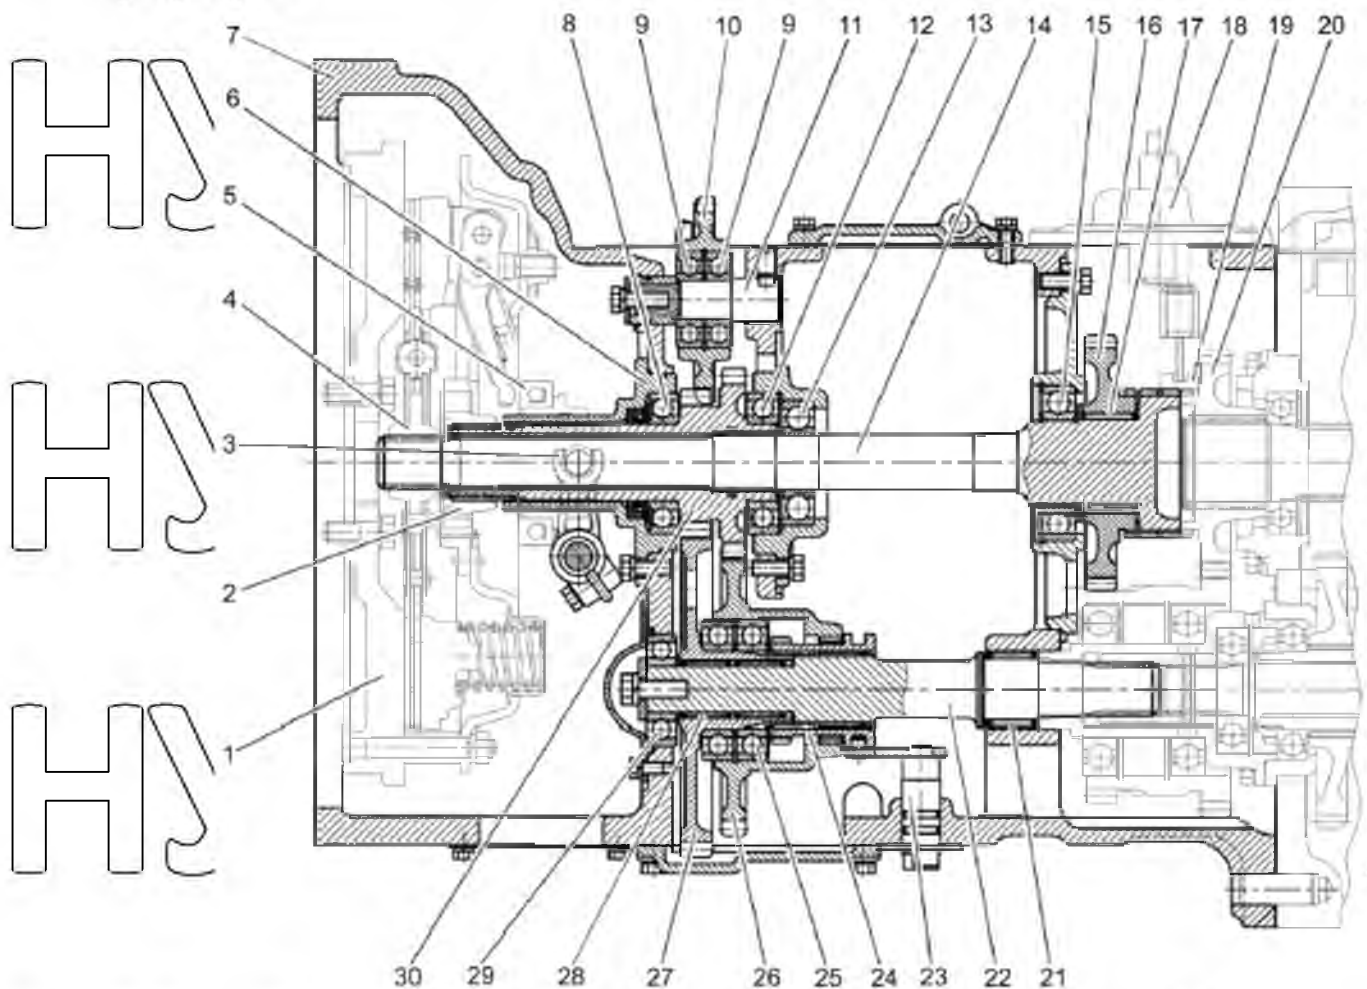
Корпус зчеплення з підвищуючим редуктором (або зі
